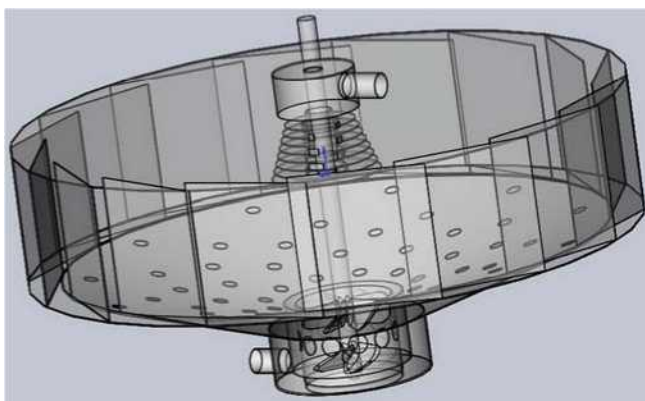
Вихревая камера с дисковым распылителем и прозрачными стенками
